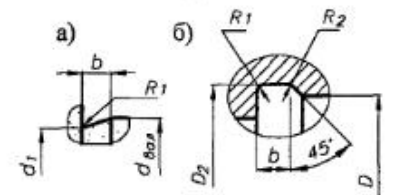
Размеры подточек: а) для вала; б) для корпуса
